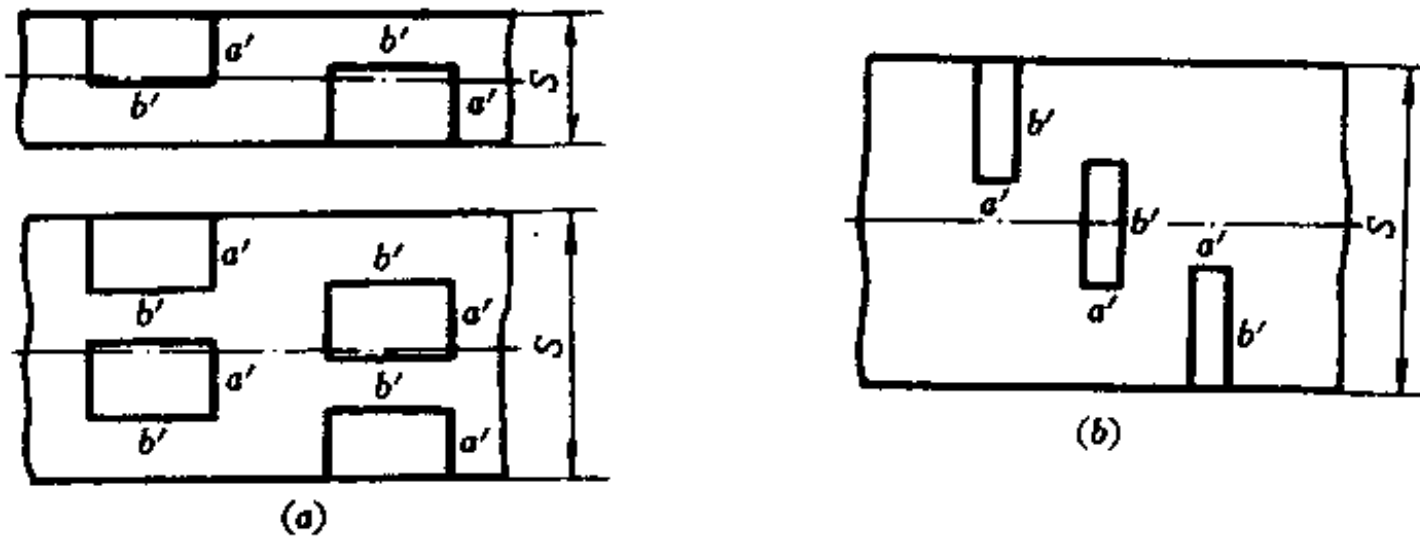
焊接接头弯曲样坯的截取方位
